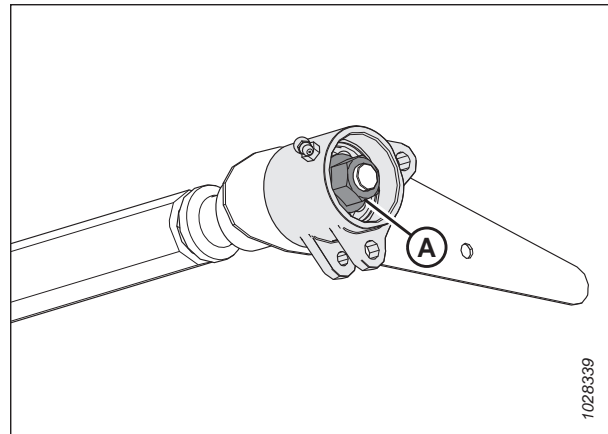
Rodamiento del rodillo tensor izquierdo
